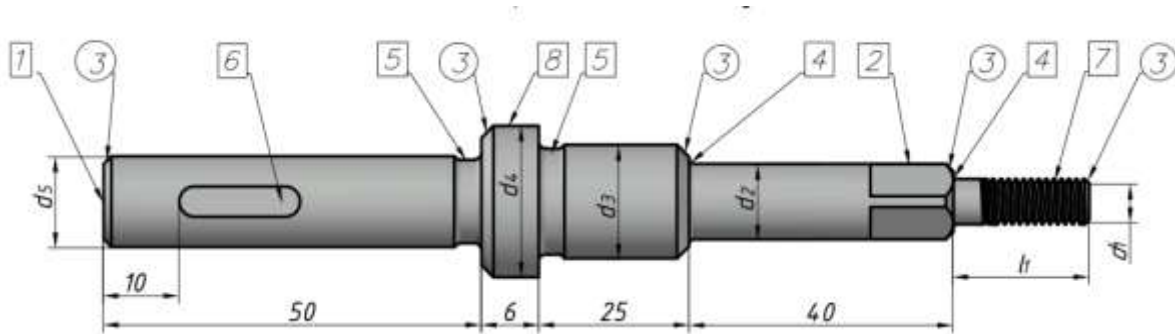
Зображення деталі для виконання робочого кресленника «Вал»
